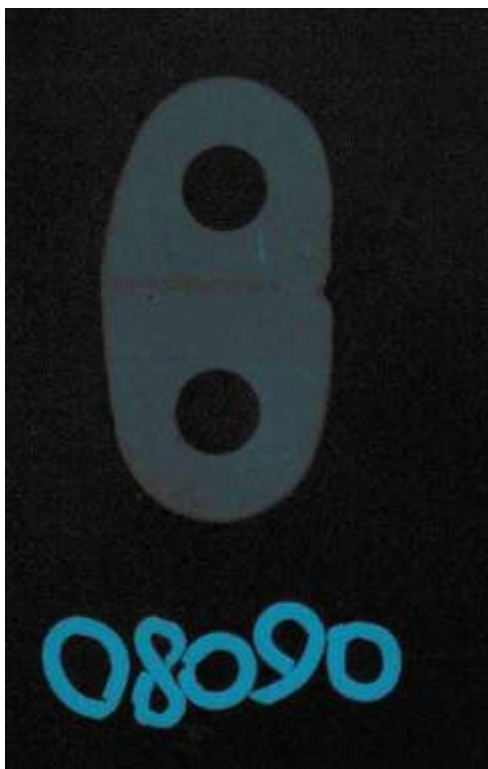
Рентгеновский снимок сварного шва
